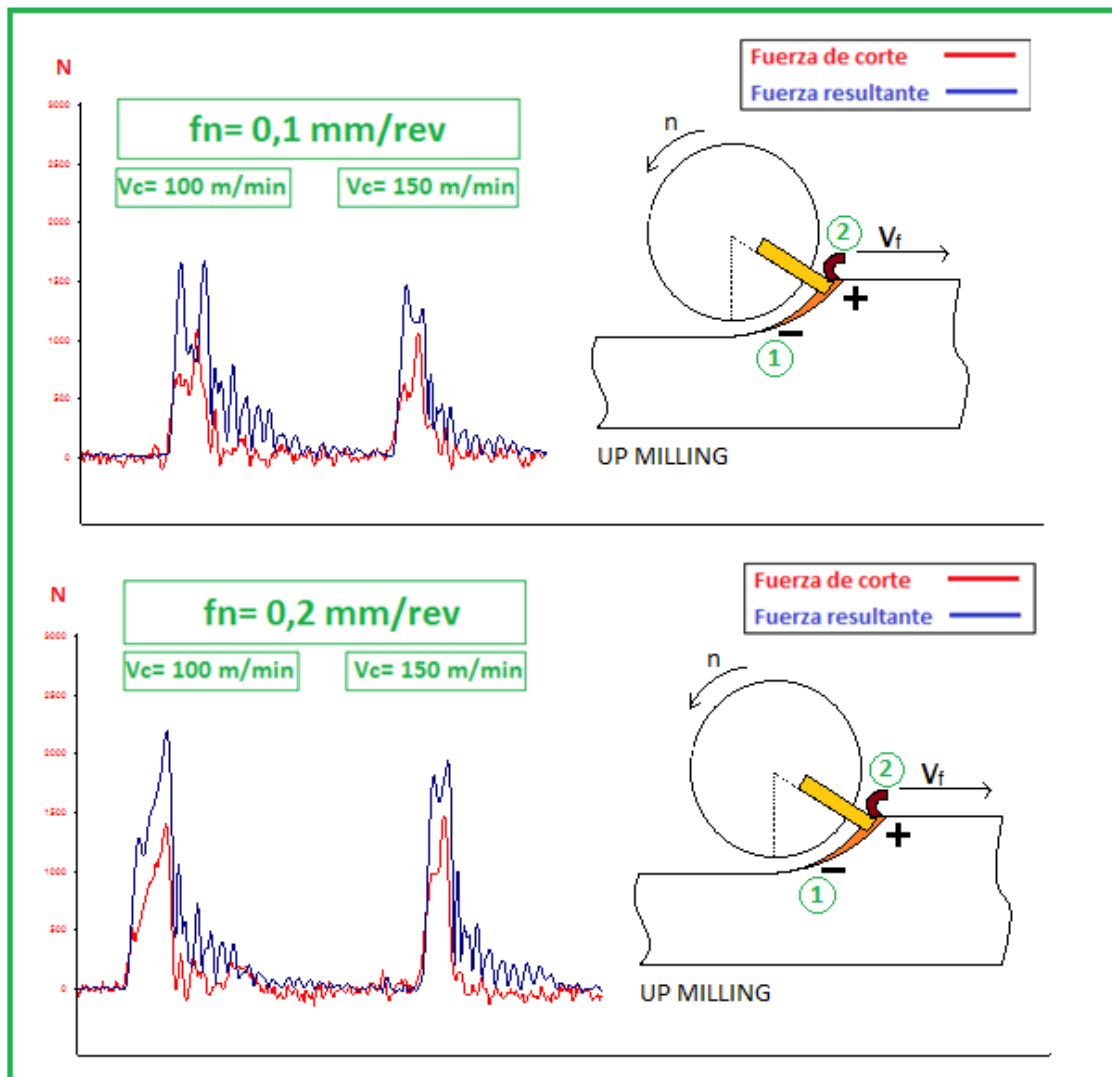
Comparación entre fuerzas de corte (F_c) y fuerzas resultantes (R) para: Fresado en oposición (UP milling) con unas condiciones de mecanizado: $f_n = 0,1 \text{ mm/rev}$ y aumentando la velocidad de corte pasando de 100 (m/min) a 150 (m/min). En la parte inferior haciendo la misma variación de velocidad de corte, pero para un avance por revolución de 0,2 mm/rev
